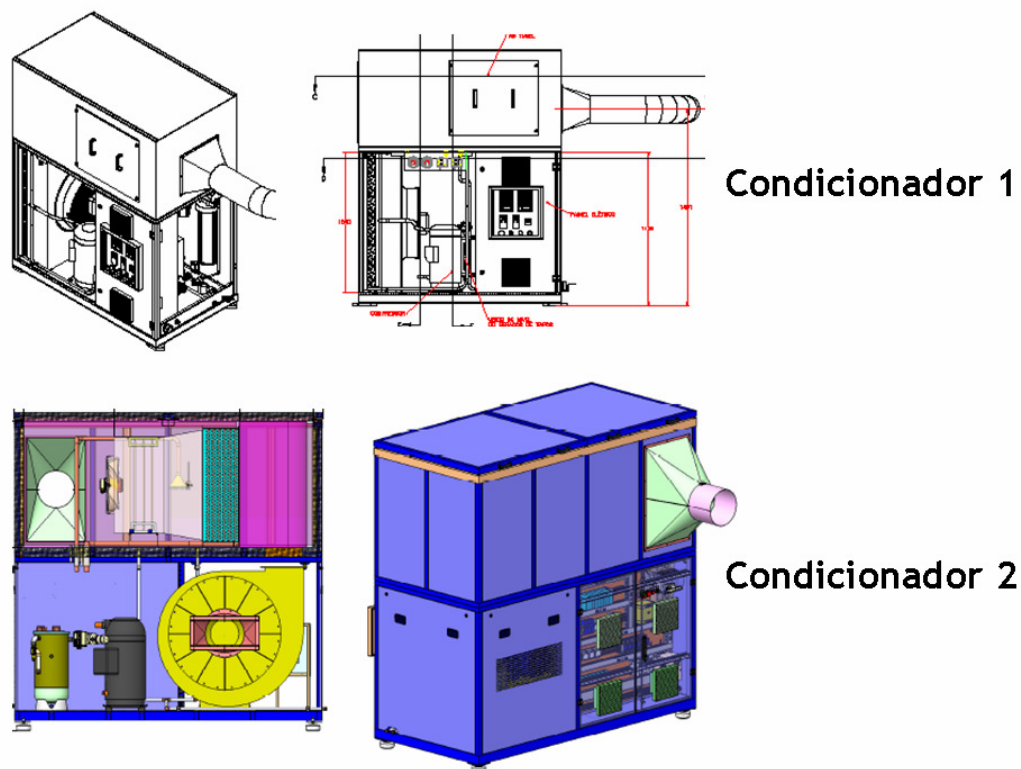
Desenho Dimensional dos Condicionadores de Ar 1 e 2
